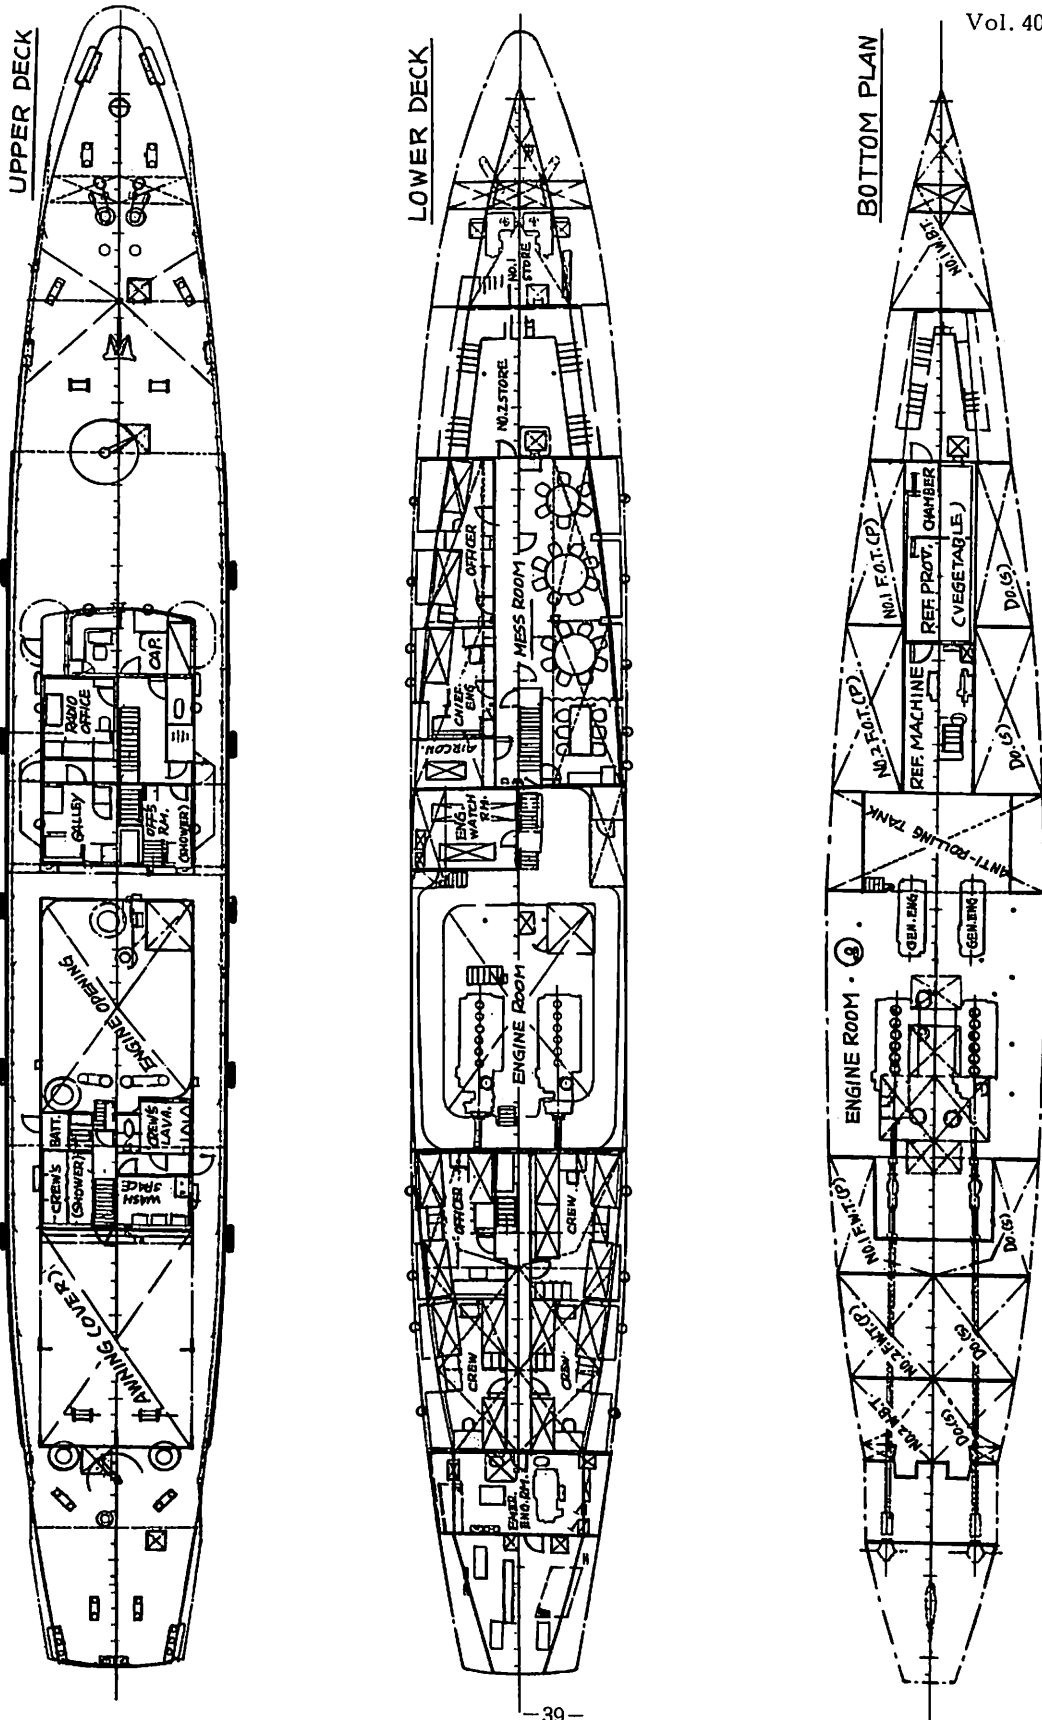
中国向け新鋭海上救助船“津監巡5”一般配置図
